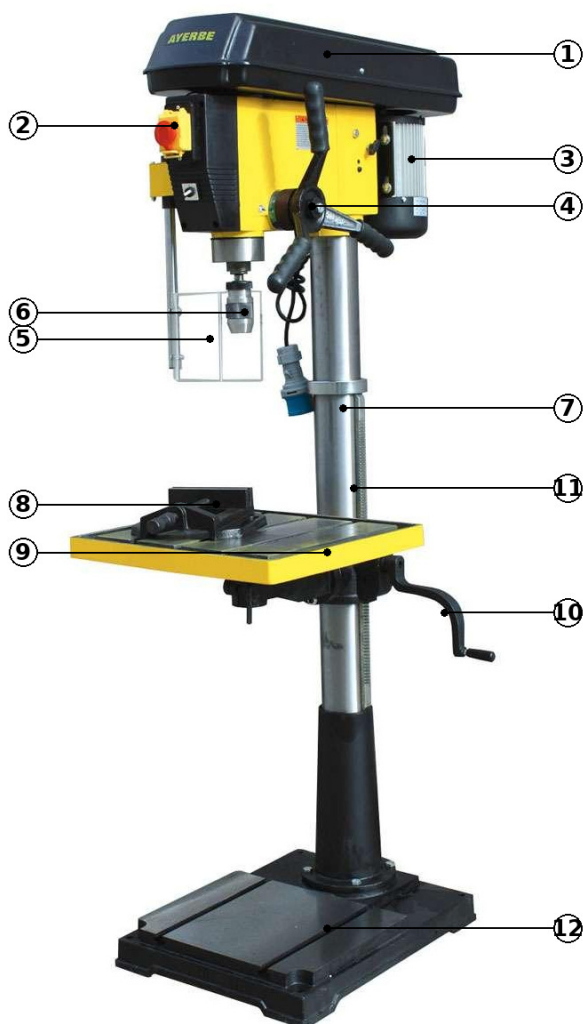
Componentes principais (AY-32 TC MN PRO)
